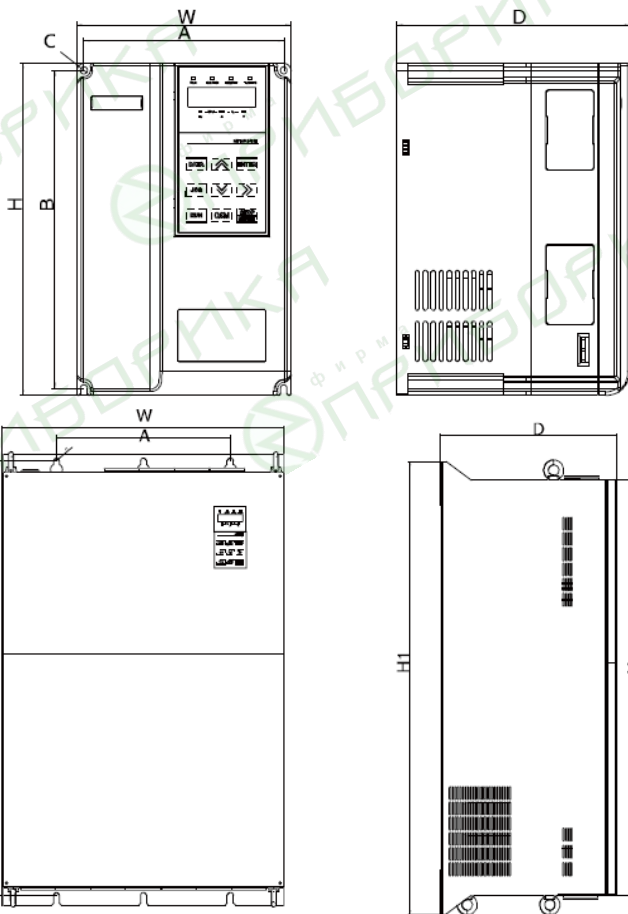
Габаритные и монтажные размеры Преобразователя 200MN[03] в металлическом корпусе
